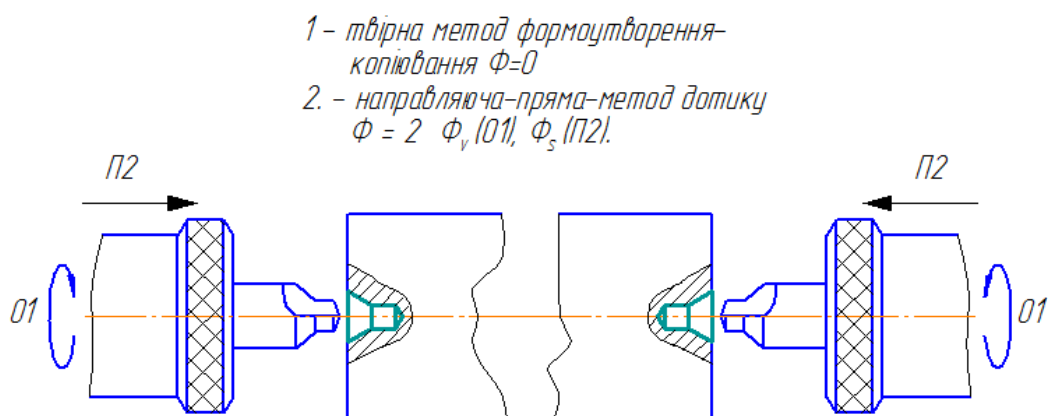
Комплекс формоутворюючих рухів при обробці нерухомої заготовки центральними свердлами
